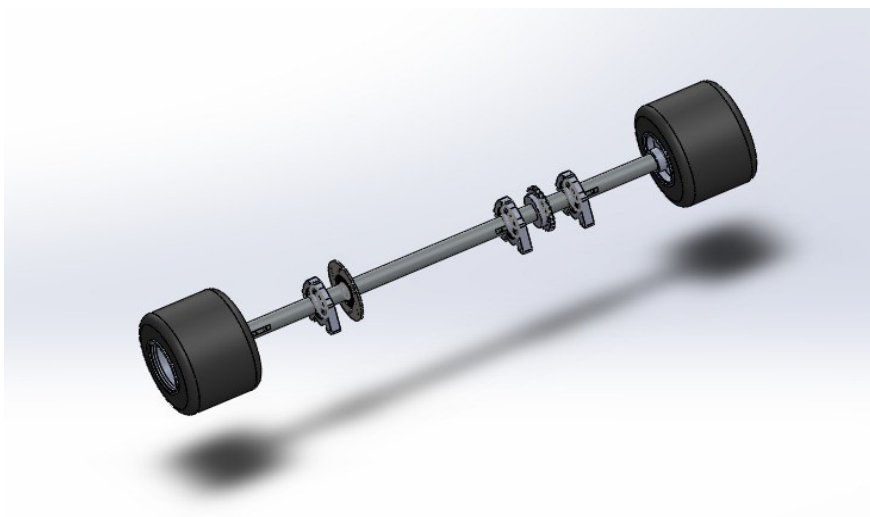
Vista isométrica do eixo com dos seus elementos montados.
